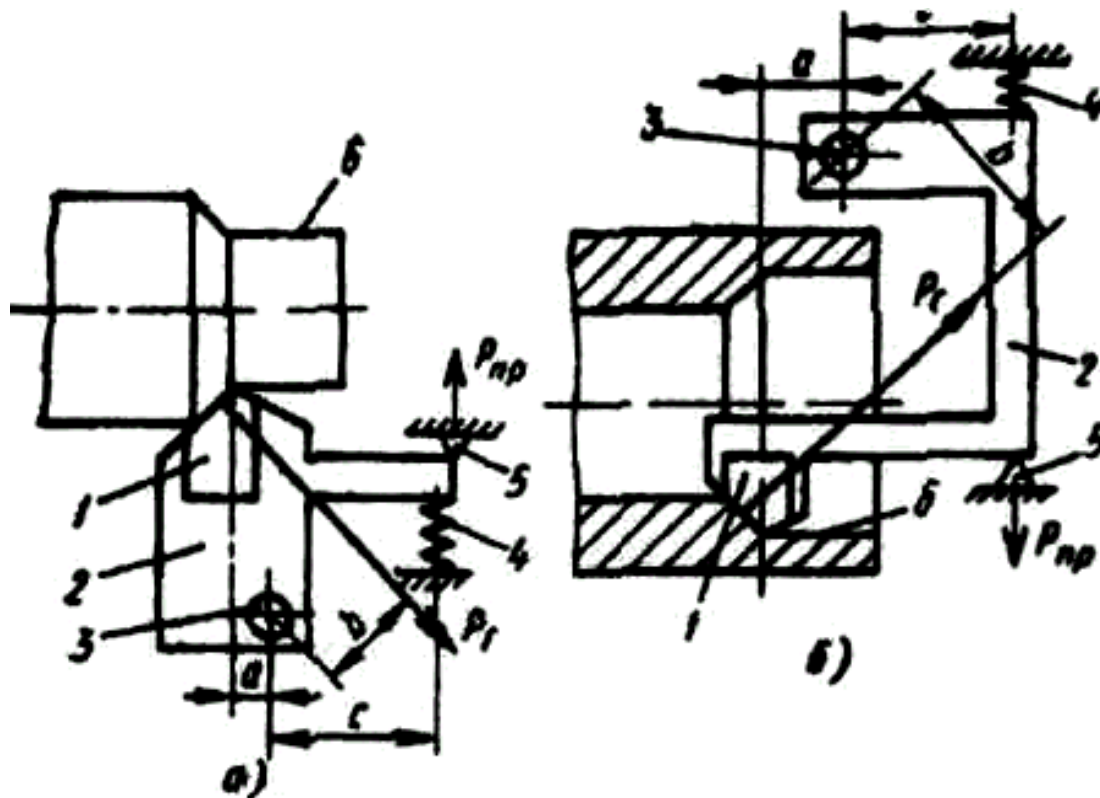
Принципова схема інструментального оснащення з від'ємною жорсткістю для обробки: а - зовнішньої; б – внутрішньої
